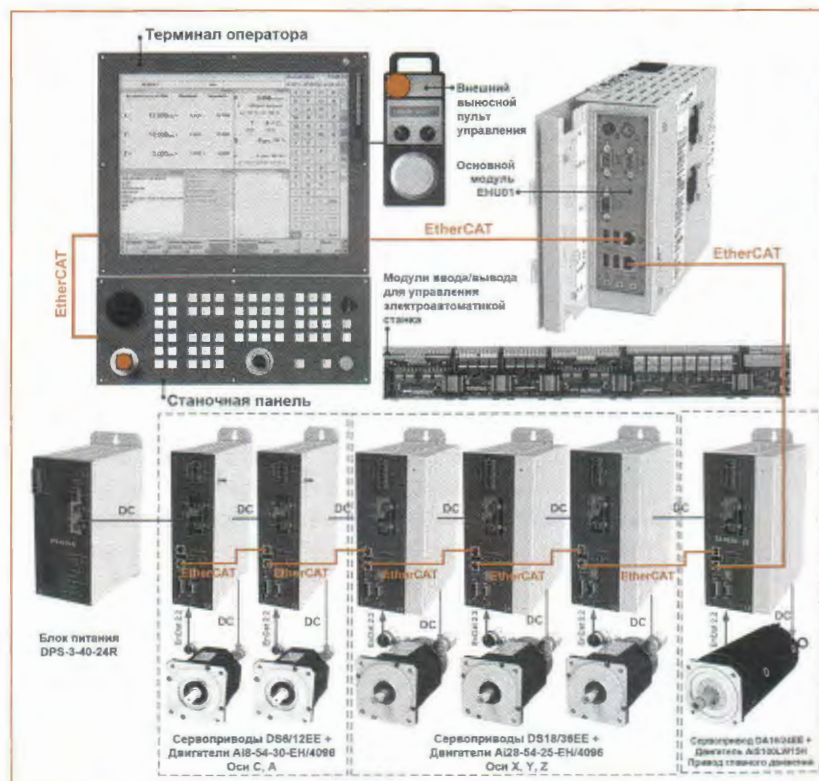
Комплект оборудования СТАНКИН NC для оснащения обрабатывающего центра
